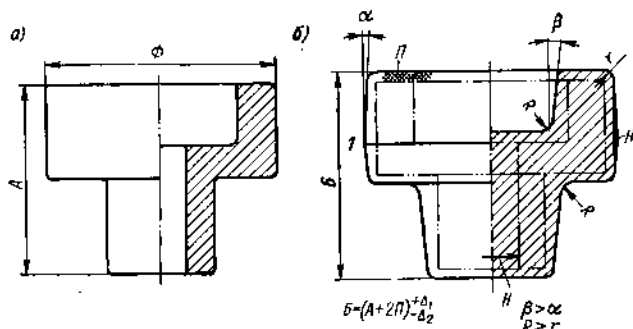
Пример составления чертежа поковки: а — деталь; б — поковка;
